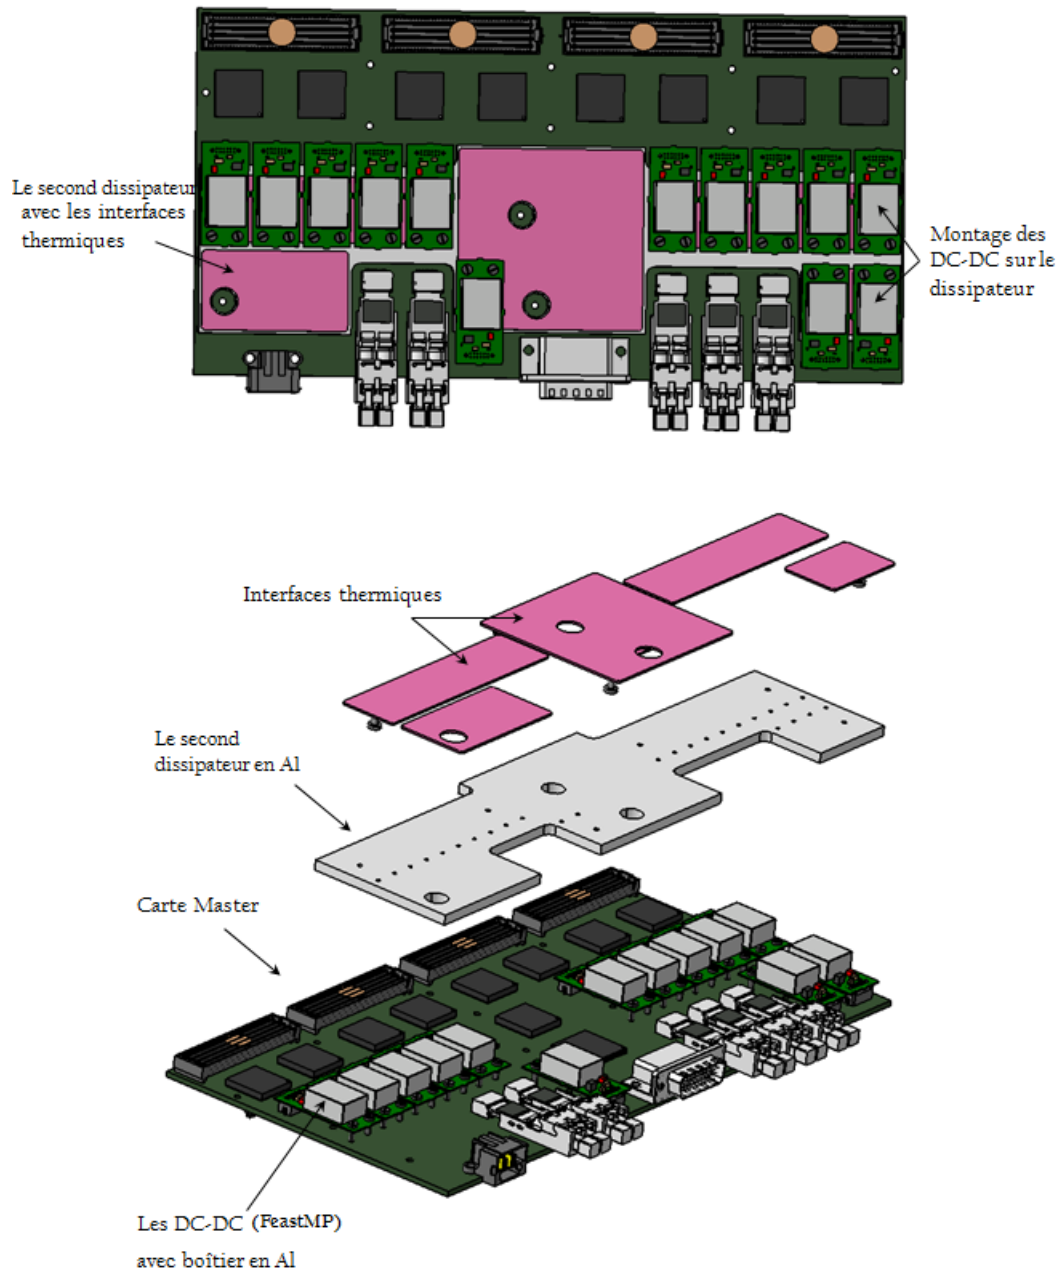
Montage du second dissipateur en aluminium sur la carte Master.
